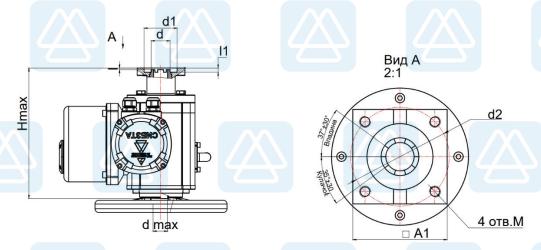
Присоединительные размеры электропривода А-70-150, Б-200,300, В-600-1200
